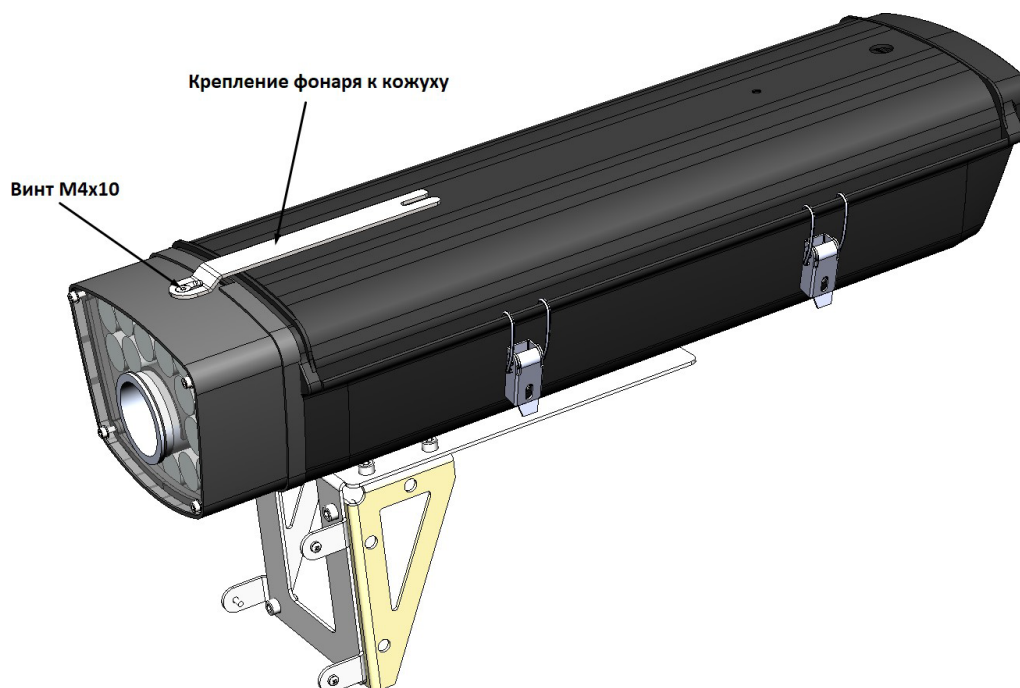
Установка Крепления фонаря к кожуху на ИК-прожектор
